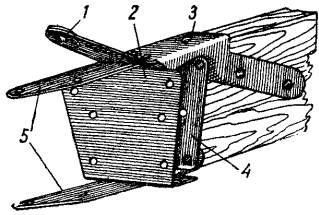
Передний узел крепления нижнего крыла (левый). 1—ушко крепления задней несущей ленты-расчалки; 2—стенка; 3—обойма узла; 4—ушко для крепления нижней ленты-расчалки; 5—пластина для крепления крыла к фюзеляжу.
